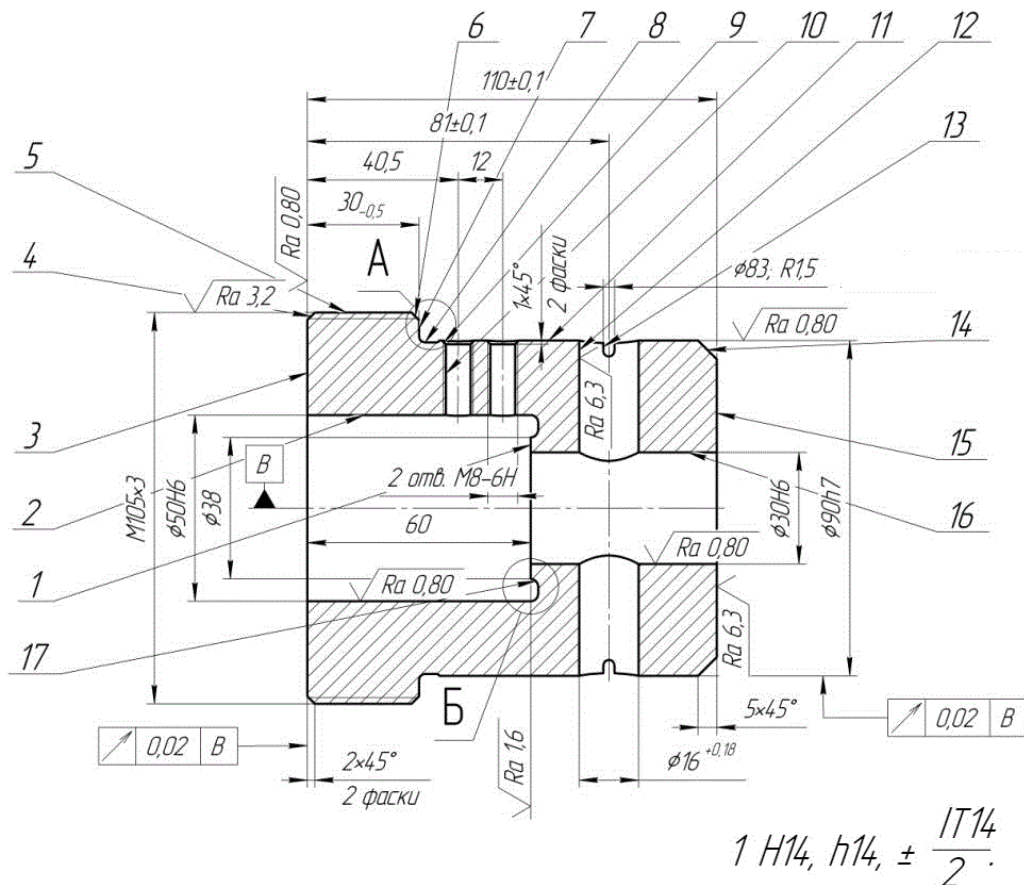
Схема конструкції деталі “Стакан”
